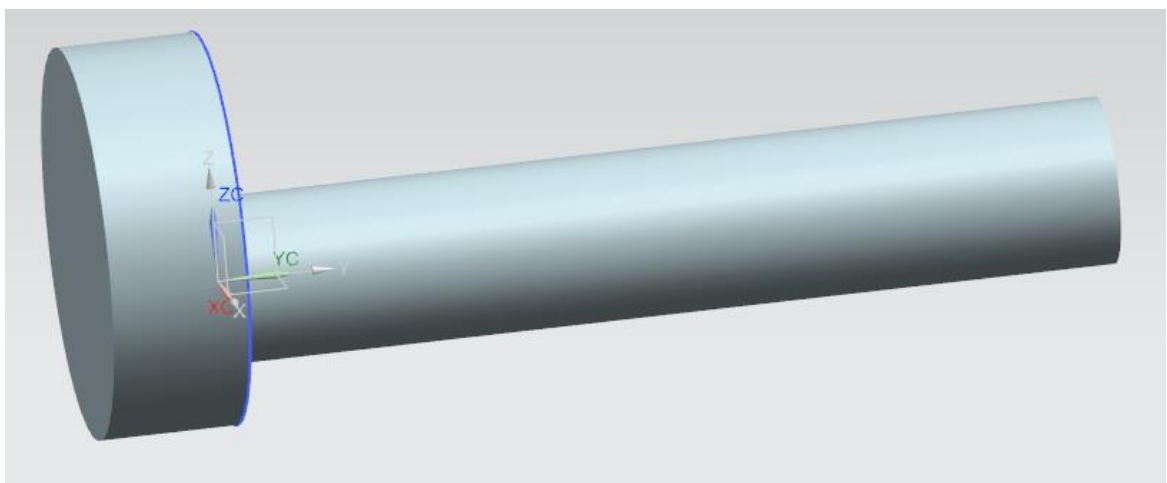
Изображение детали после построения корпуса улитки
